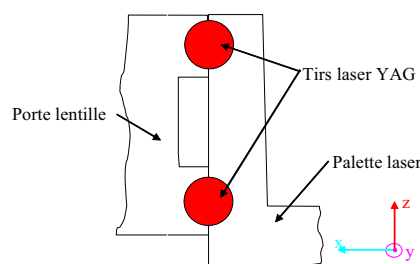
Représentation schématique des deux éléments, palette laser et porte-lentille1, soudé par tirs laser Nd : YAG
